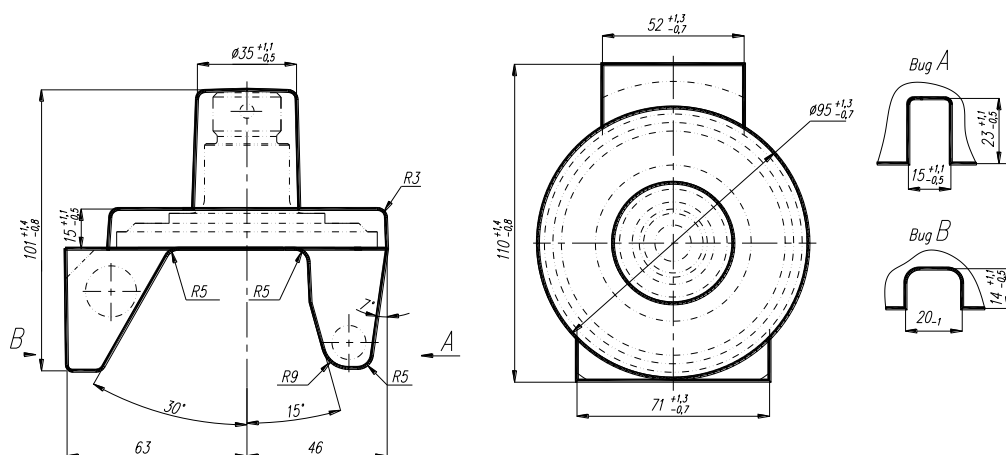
Ескіз заготовки деталі “Піввісь”
